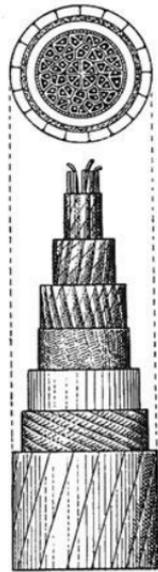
Aufbau eines 28 paarigen Fernsprechröhrenkabels mit geschlossener Bewehrung.
